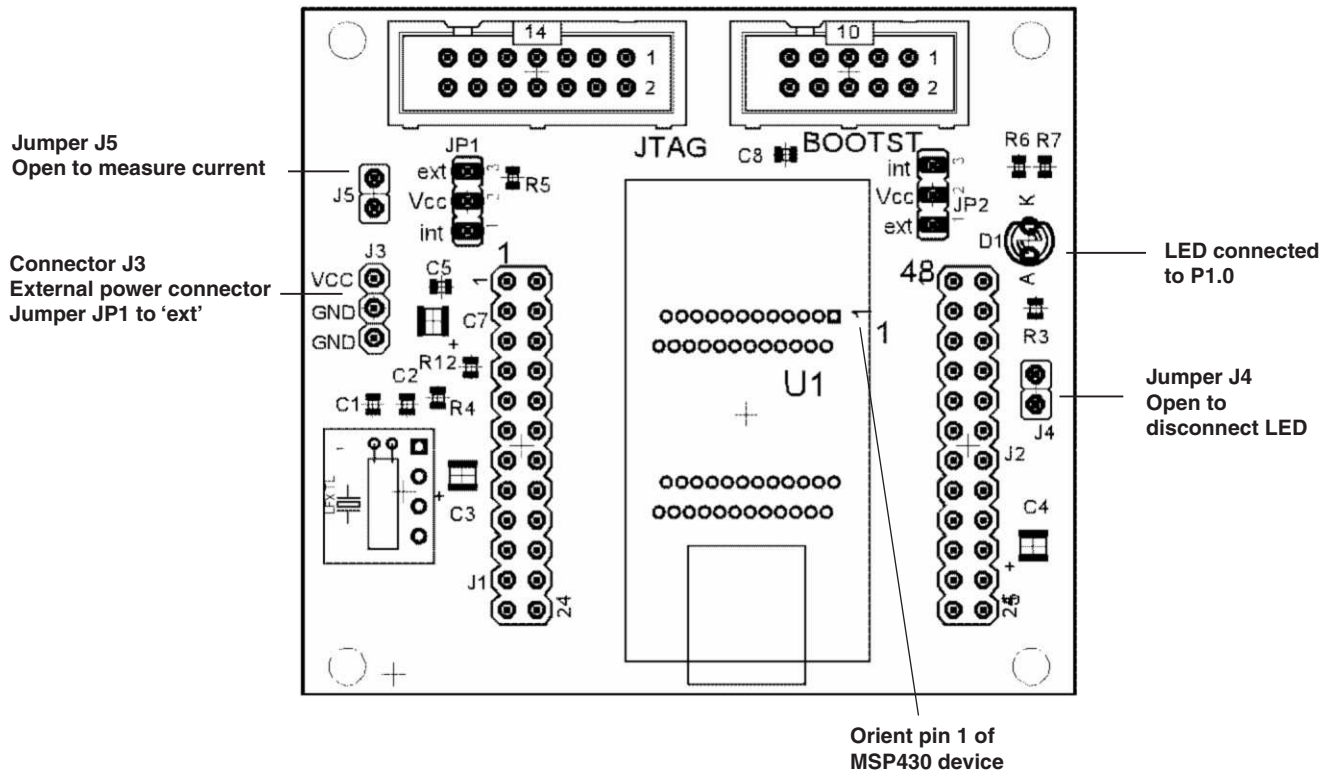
MSP-TS430DL48 目标插座模块, PCB
